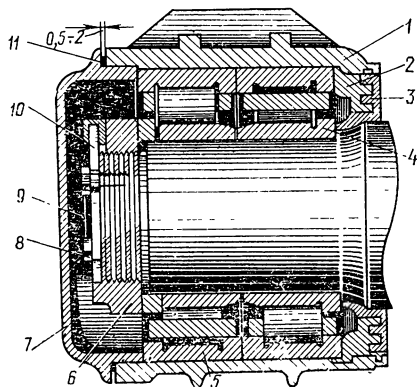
Букса грузового вагона с двумя цилиндрическими подшипниками на горячей посадке:
